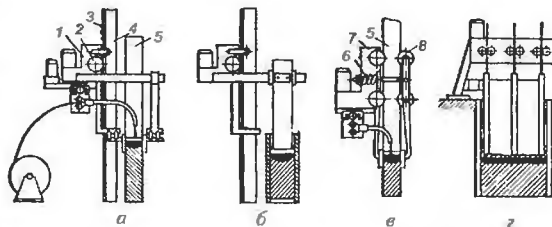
Принципові схеми будови апаратів для електрошлакового зварювання:
